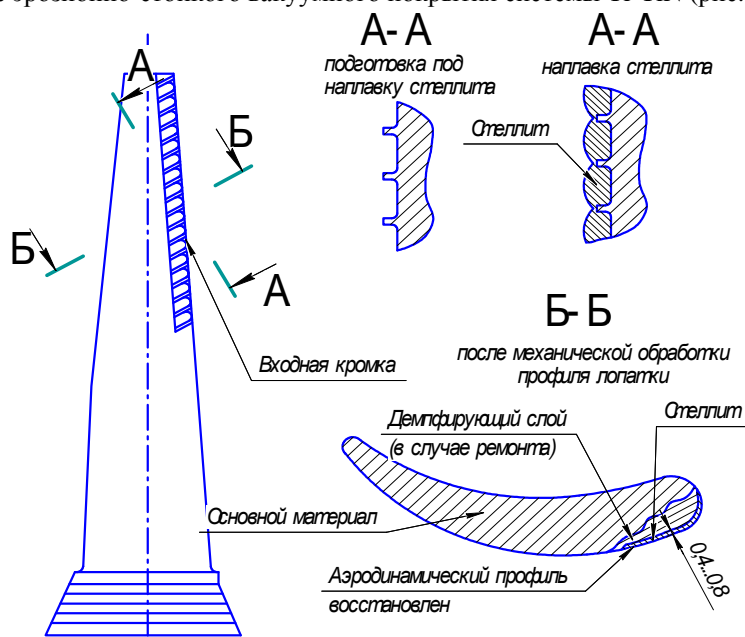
Схема подготовки поверхности и матричного упрочнения входной кромки лопатки
